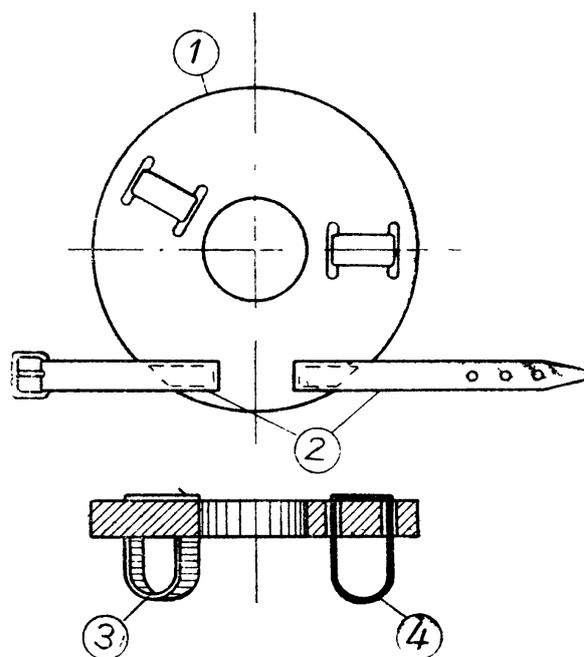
Предохранитель при рубке 1—кожаный кружок; 2—ремень для кисти рук; 3—петля для указательного пальца; 4—петля для большого пальца
